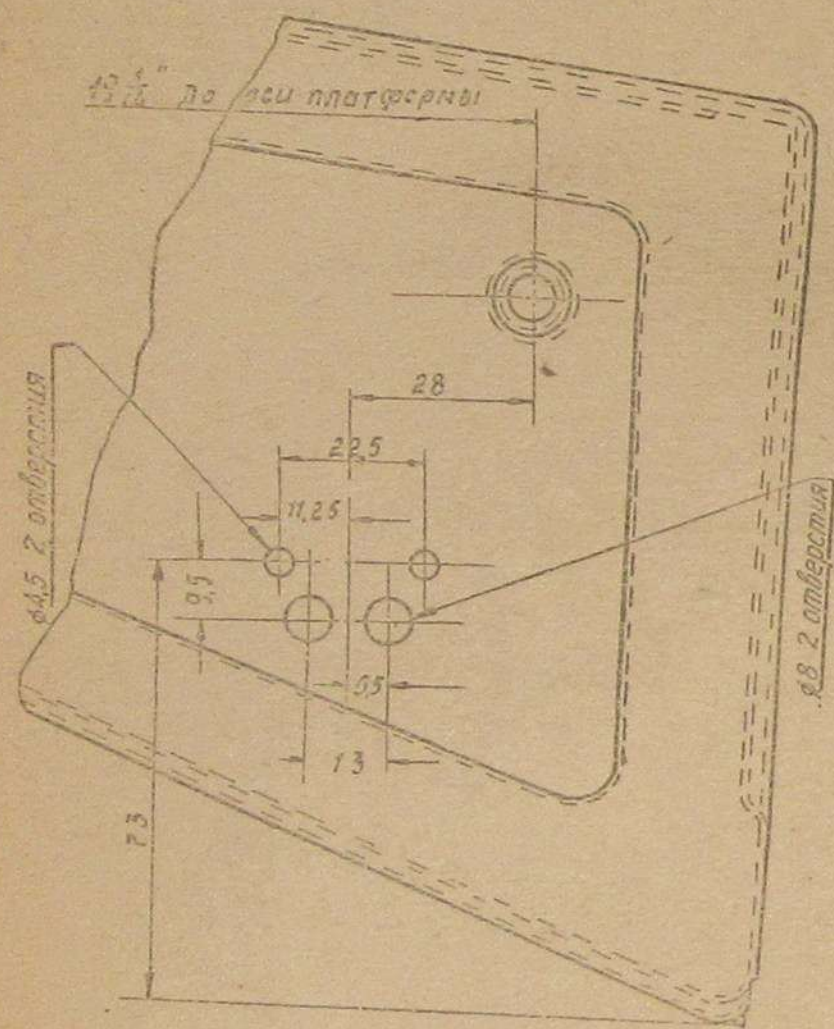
Передняя панель кабины автомобиля ГАЗ с разметкой отверстий для установки выключателя электромотора вентилятора.
